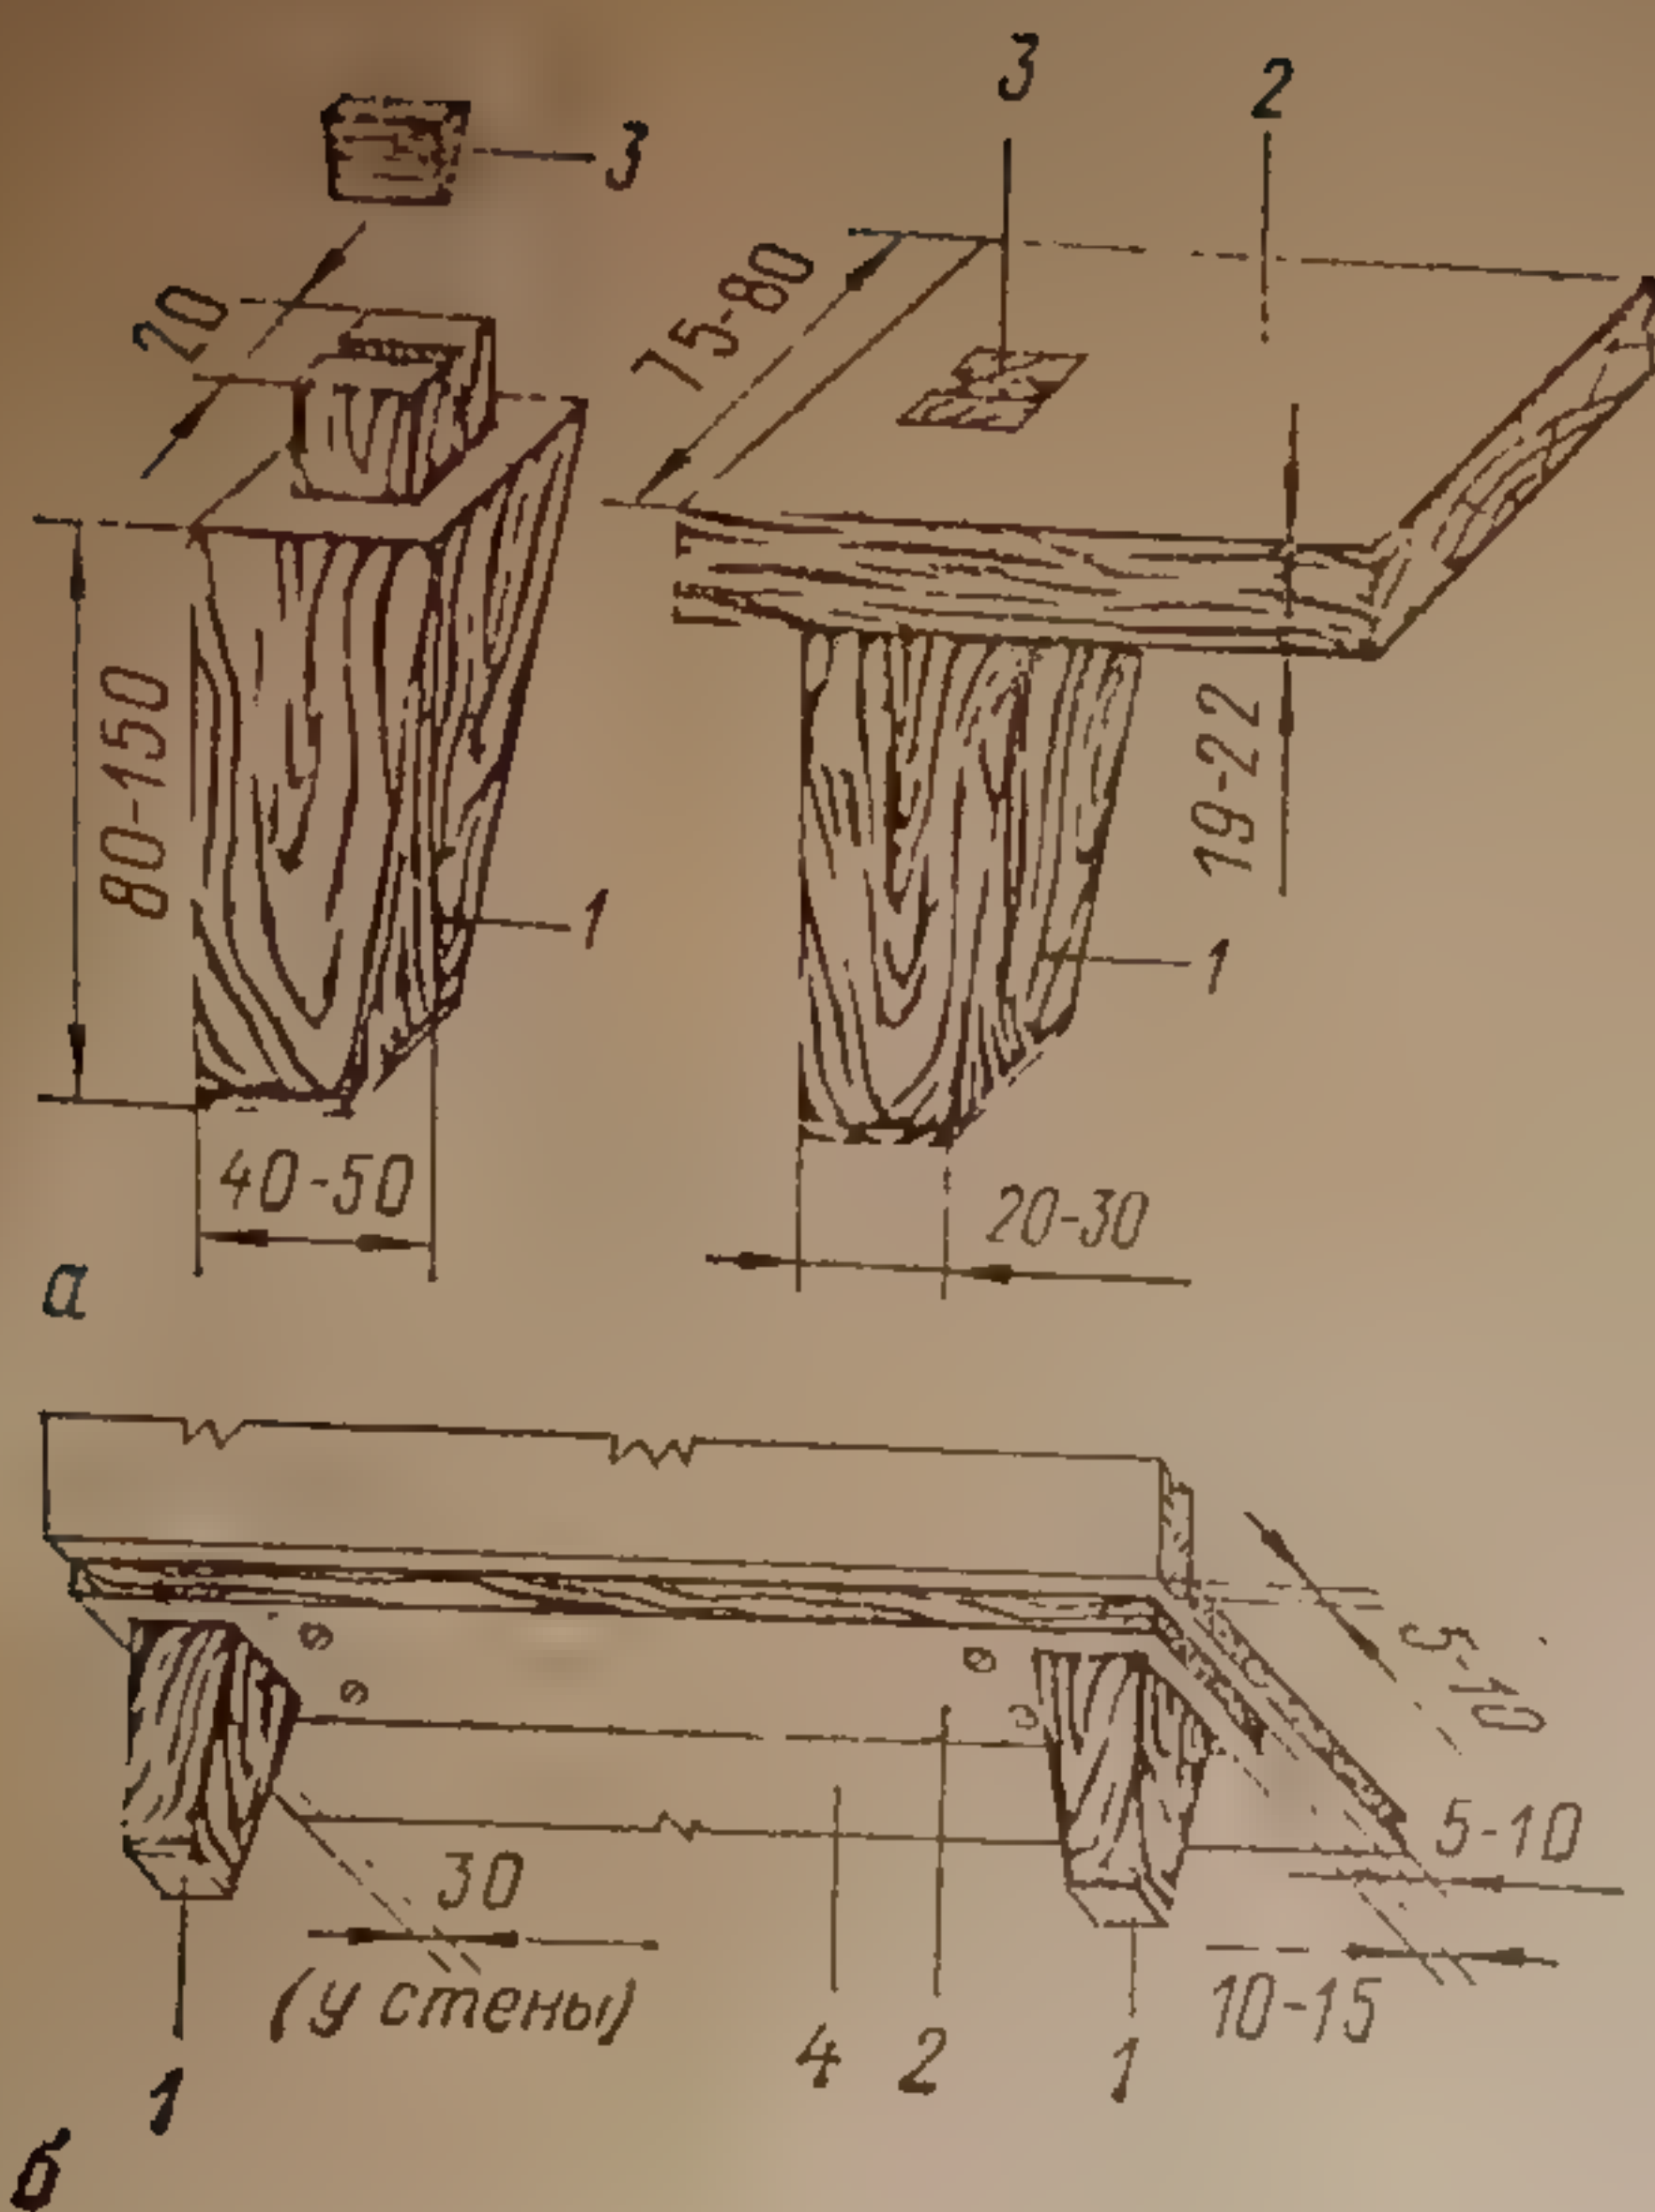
Ножки: а — соединение ножки с накладкой; б — крепление накладки к днищу; 1 — ножка; 2 — накладка; 3 — клин; 4 — днище
